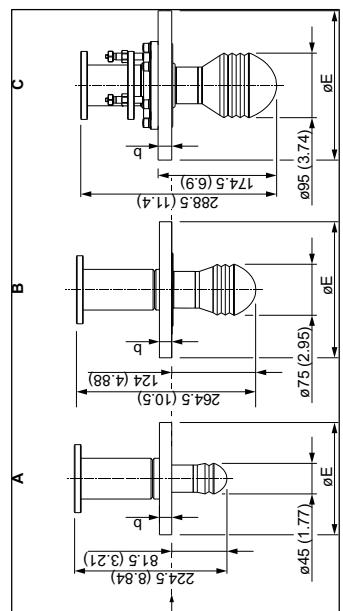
Maßblatt Antennenbaugruppen NMR81
